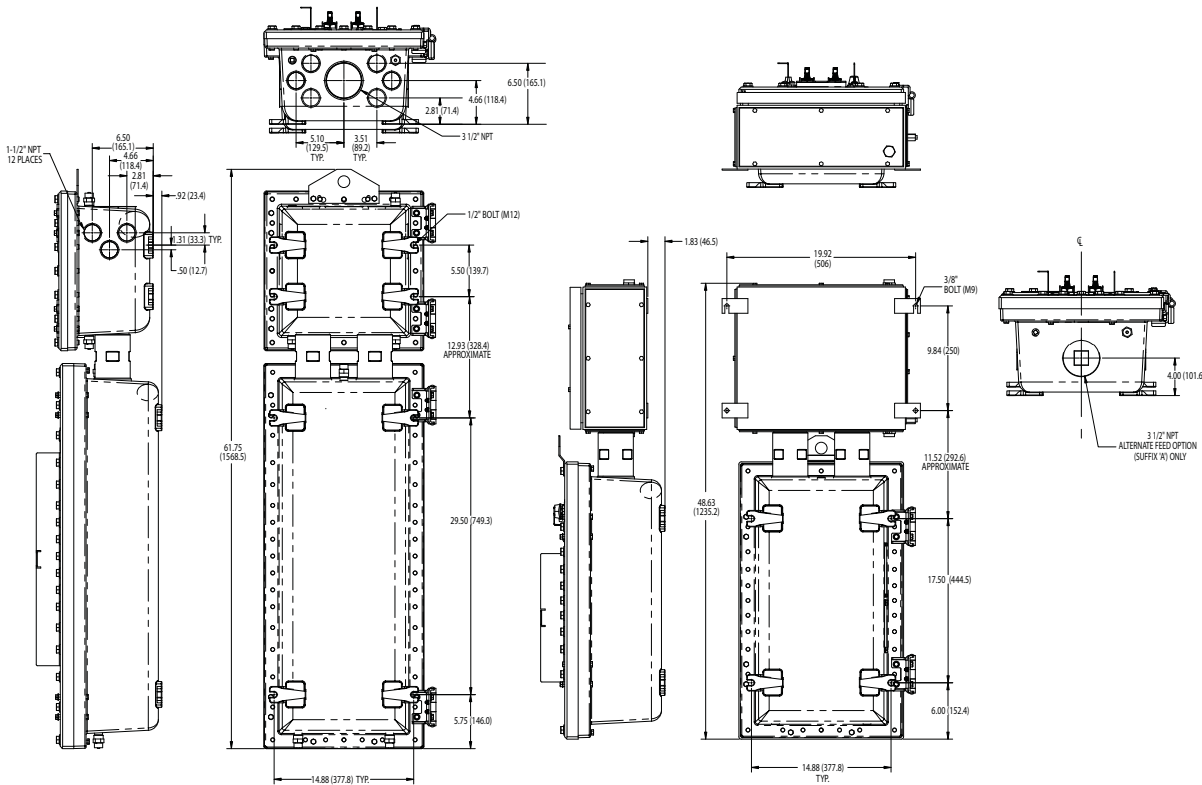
DIMENSIONES DE MONTAJE Y PESOS
